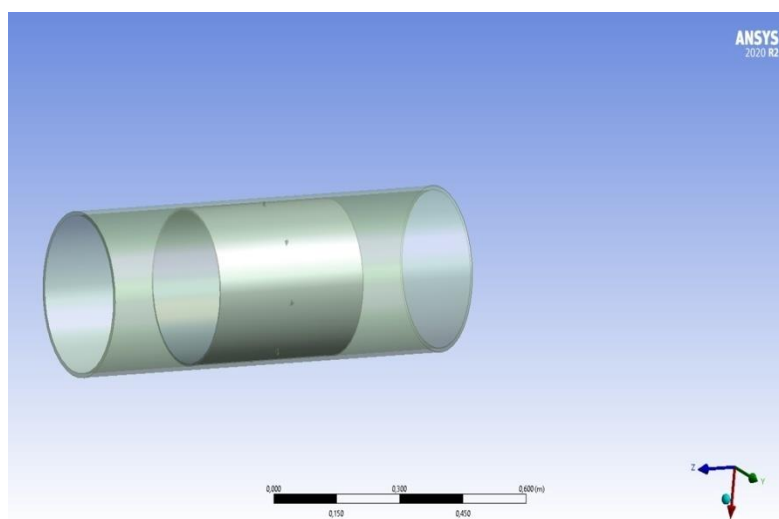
Узел сварного соединения с CPS-втулкой
